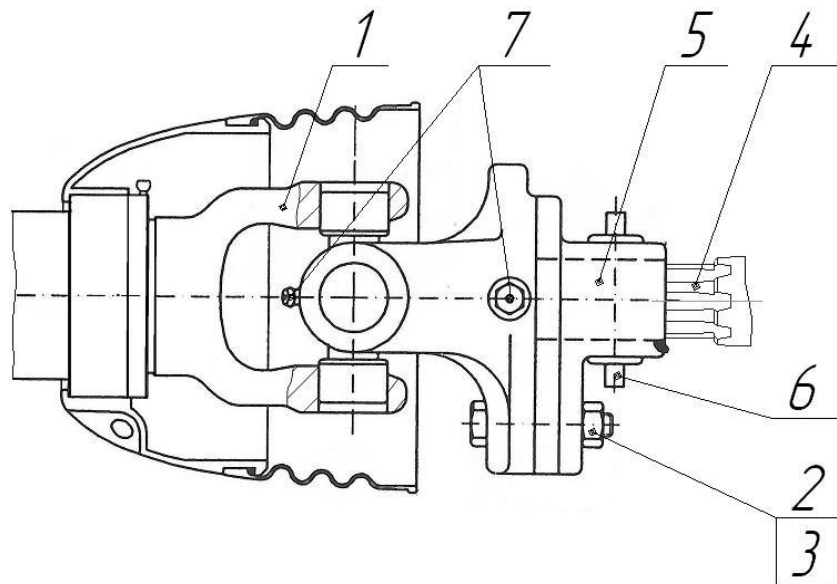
Схема смазки (машина МТУ-24А с разбрасывателем с четырьмя вертикальными барабанами)
